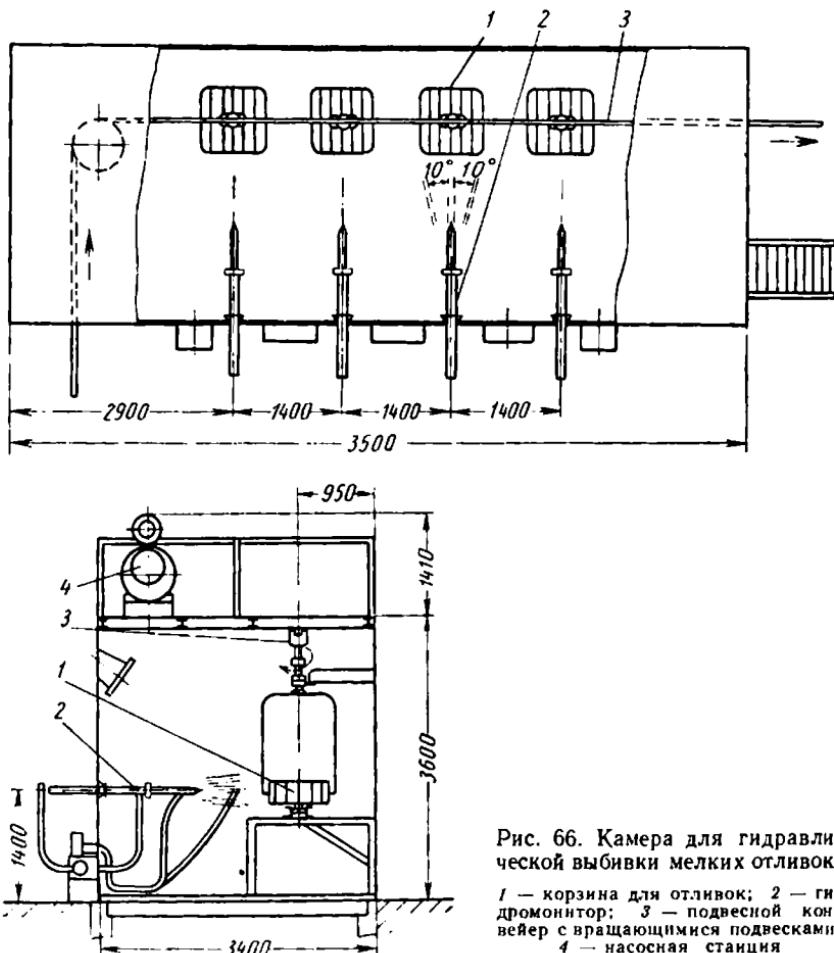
Камера для гидравлической выбивки мелких отливок:
